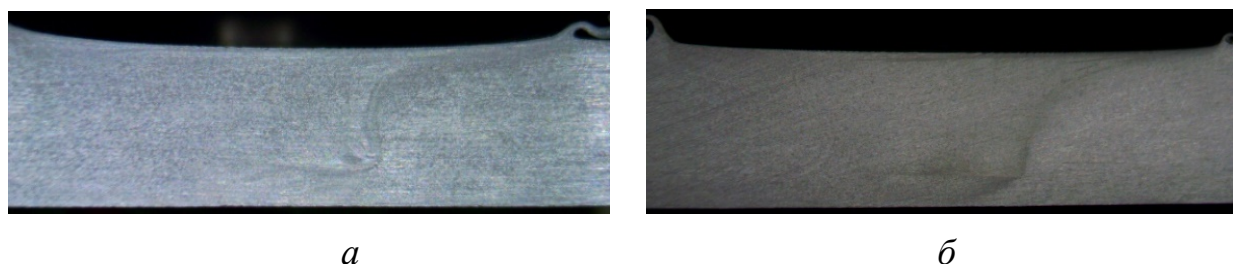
Макрошлифы поперечных сечений сварных швов, полученных с помощью инструмента с цилиндрической (*а*) и конической (*б*) формой пина: частота вращения инструмента - 710 об/мин, продольная подача инструмента (скорость сварки) - 50 мм/мин
